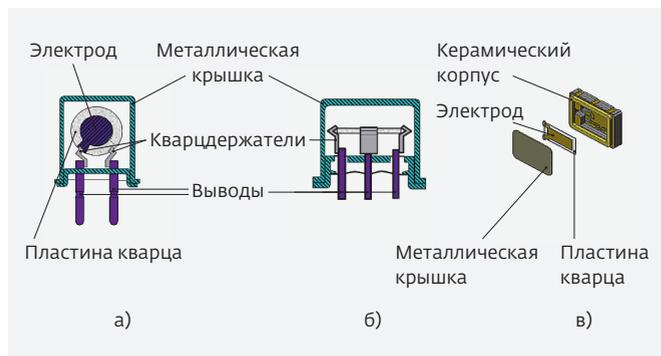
Типы корпусирования кварцевых резонаторов: двухпиновый (а) и трех- или четырехпиновый (б) металлические корпуса; керамический корпус для поверхностного монтажа (в)
